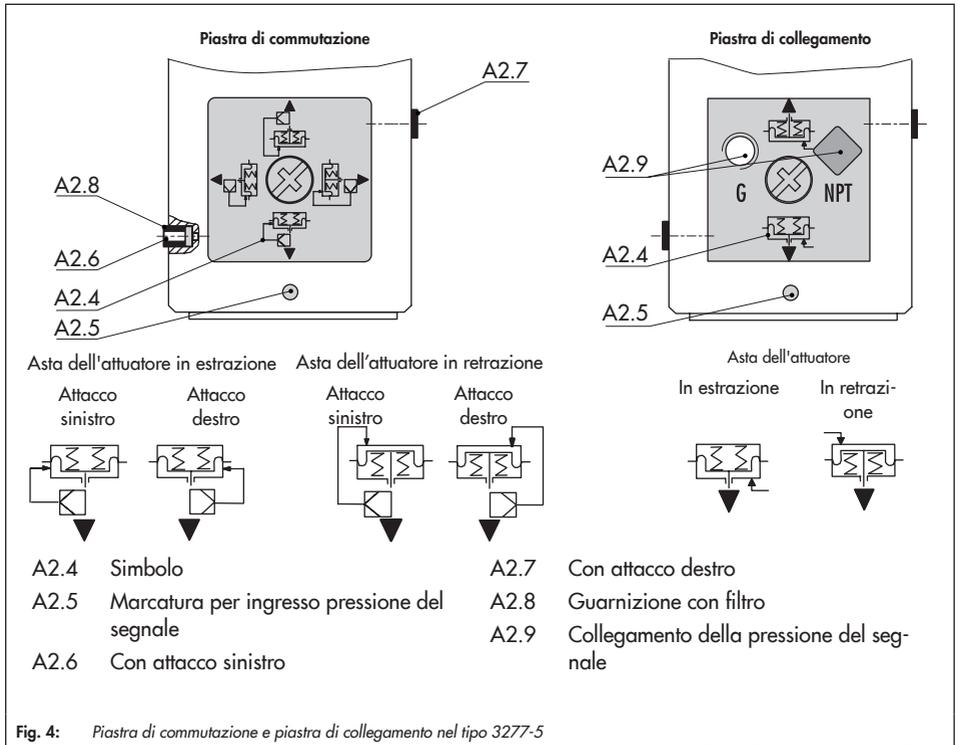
Piastra di commutazione e piastra di collegamento nel tipo 3277-5
